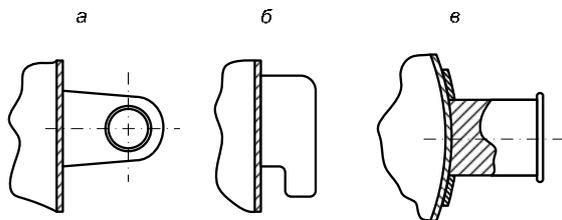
Приспособления для монтажа аппаратов:
